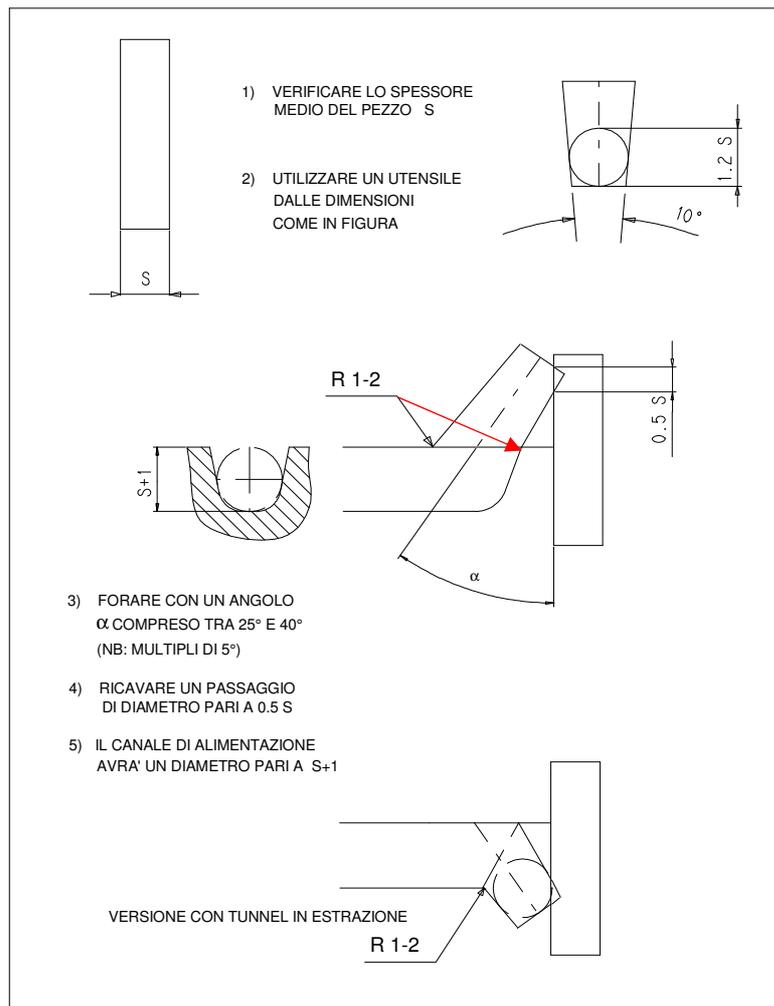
INIEZIONE A TUNNEL - REALIZZAZIONE MECCANICA
